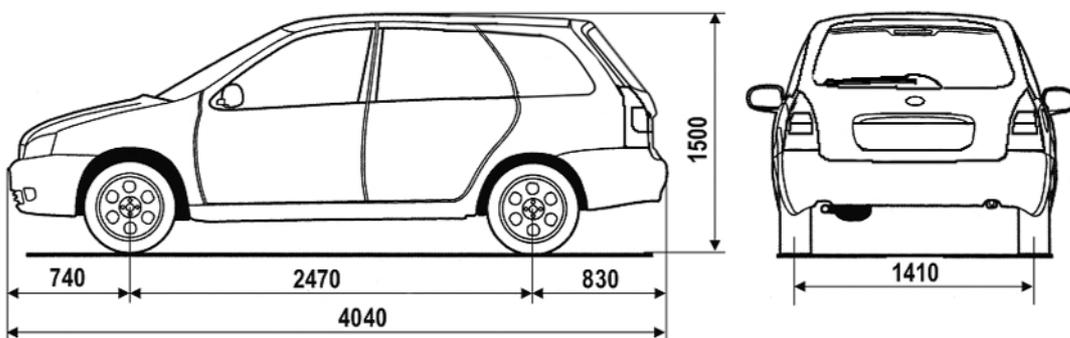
Габаритные размеры автомобиля LADA KALINA 1117.
